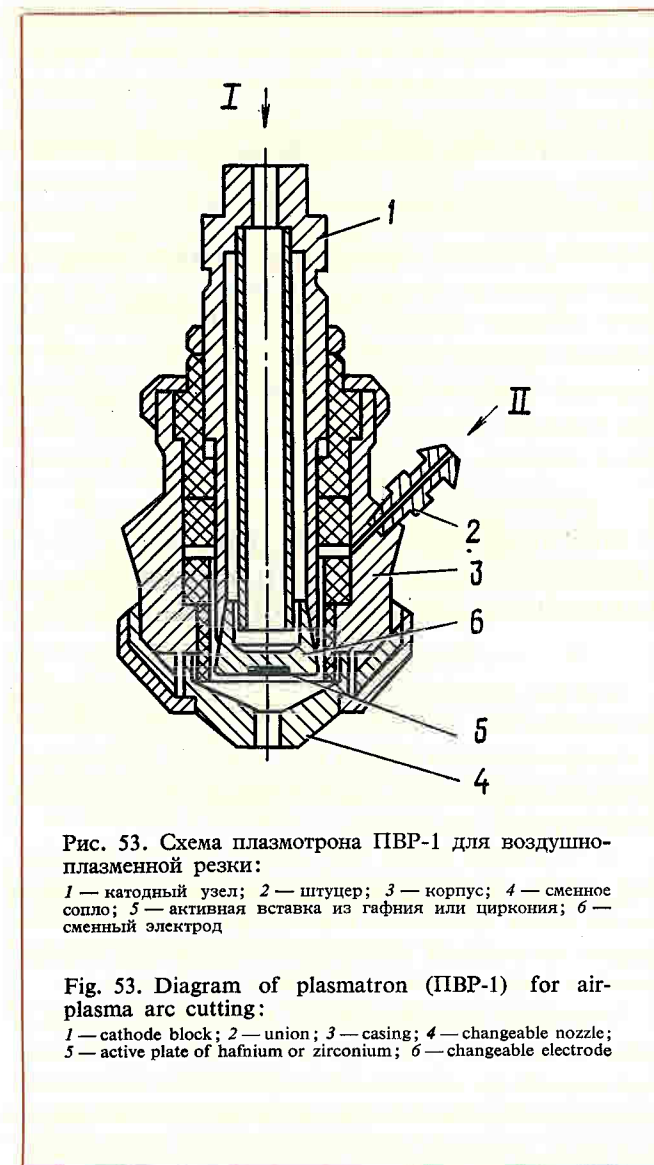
Схема плазматрона ПБР-1 для воздушно-плазменной резки:
